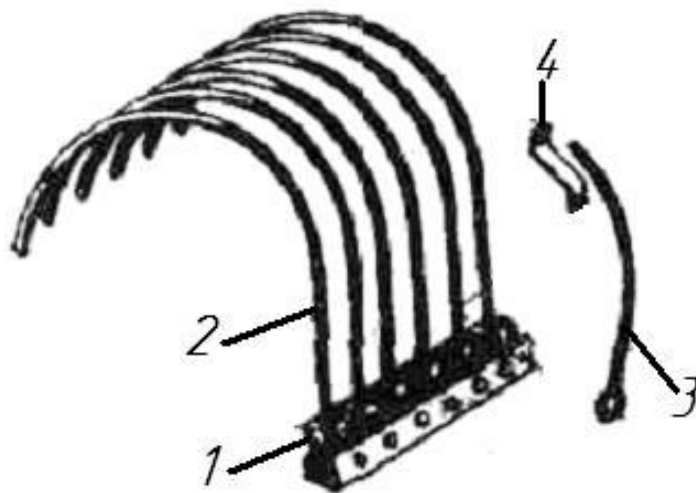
Грабельный аппарат: 1 – зубодержатель; 2 – зуб; 3 – короткий зуб
